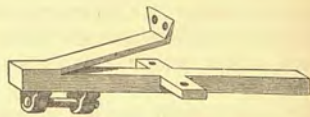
Supporto speciale per carretta lunga per trasporto botti.
